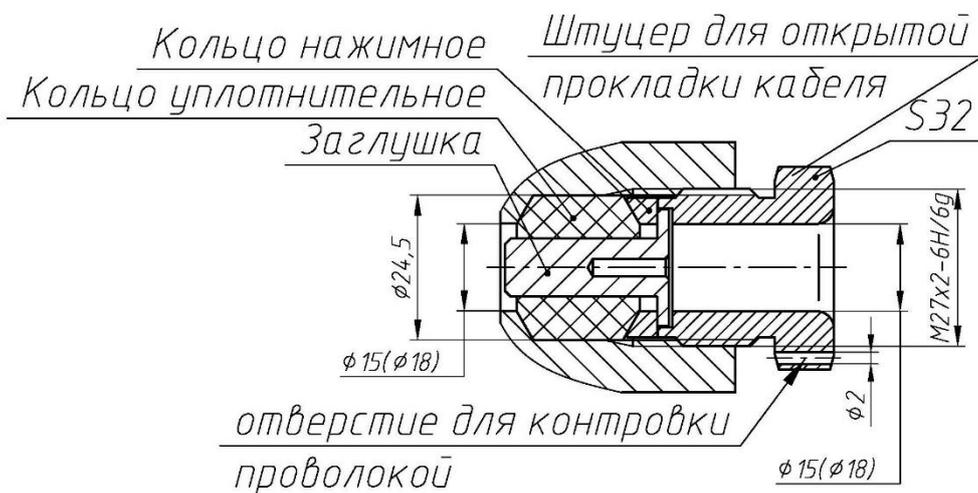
Элементы взрывозащиты кабельного ввода для открытой прокладки кабеля
